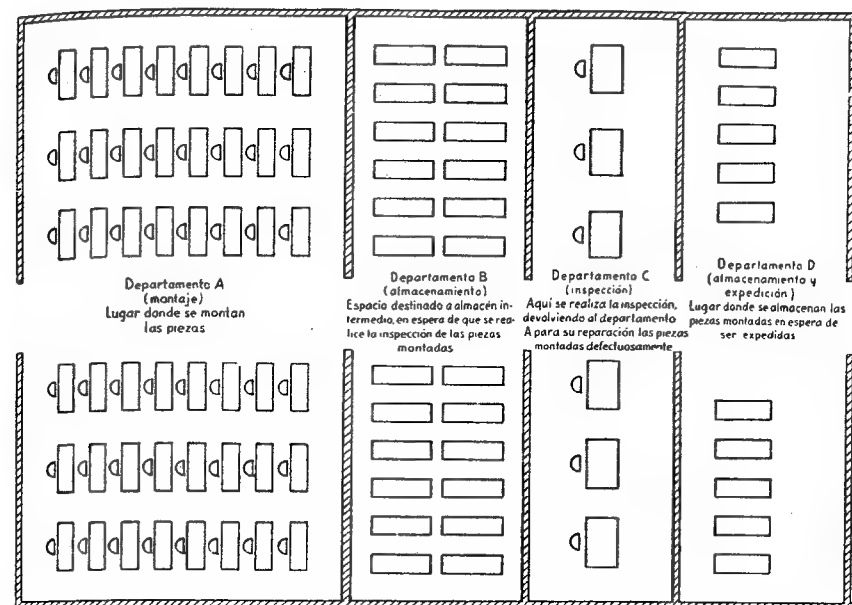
Plano del edificio destinado al montaje e inspección de piezas pequeñas producidas con máquinas semiautomáticas, según la disposición primitiva de los Departamentos. Como se observa, la inspección se realiza en el Departamento C.
